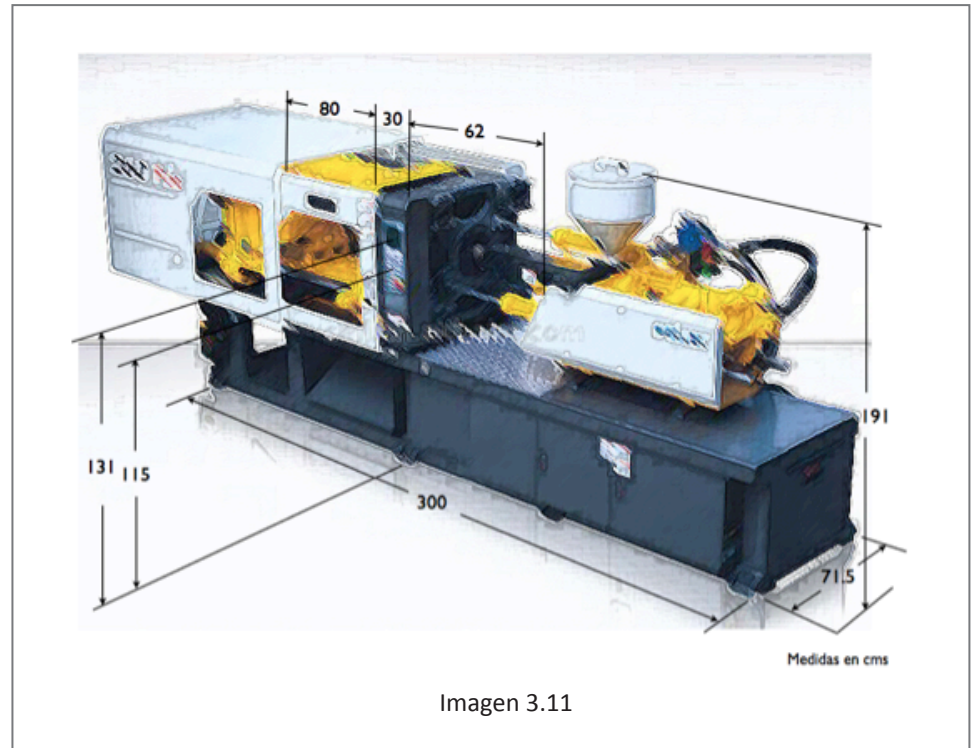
Dimensiones de la máquina más pequeña. Estación 1.
